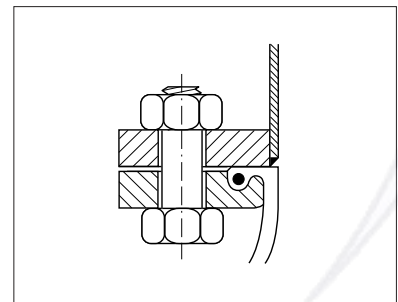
Las aristas vivas de las tuberías dañan la junta de expansión.
